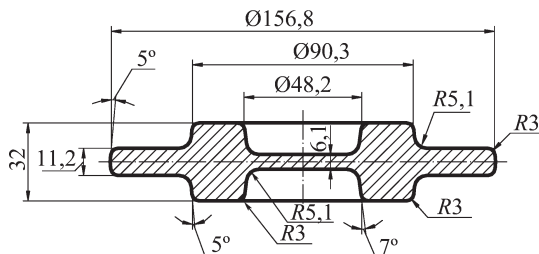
Чертеж горячей поковки (усадка — 1,5 %)
